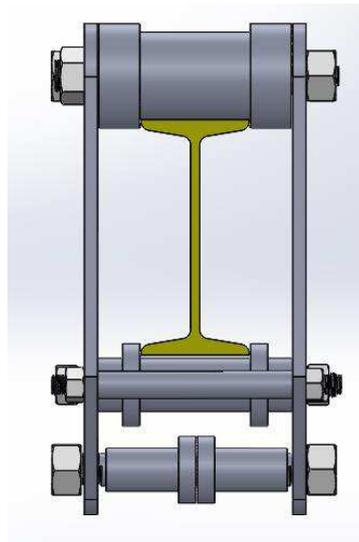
Carro apoyado sobre las alas superiores de una viga.
